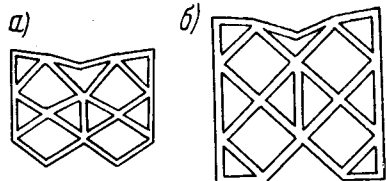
Конструкция полой резиновой прокладки с перегородками: а — вариант со скошенными нижними гранями; б — то же, с прямоугольными
